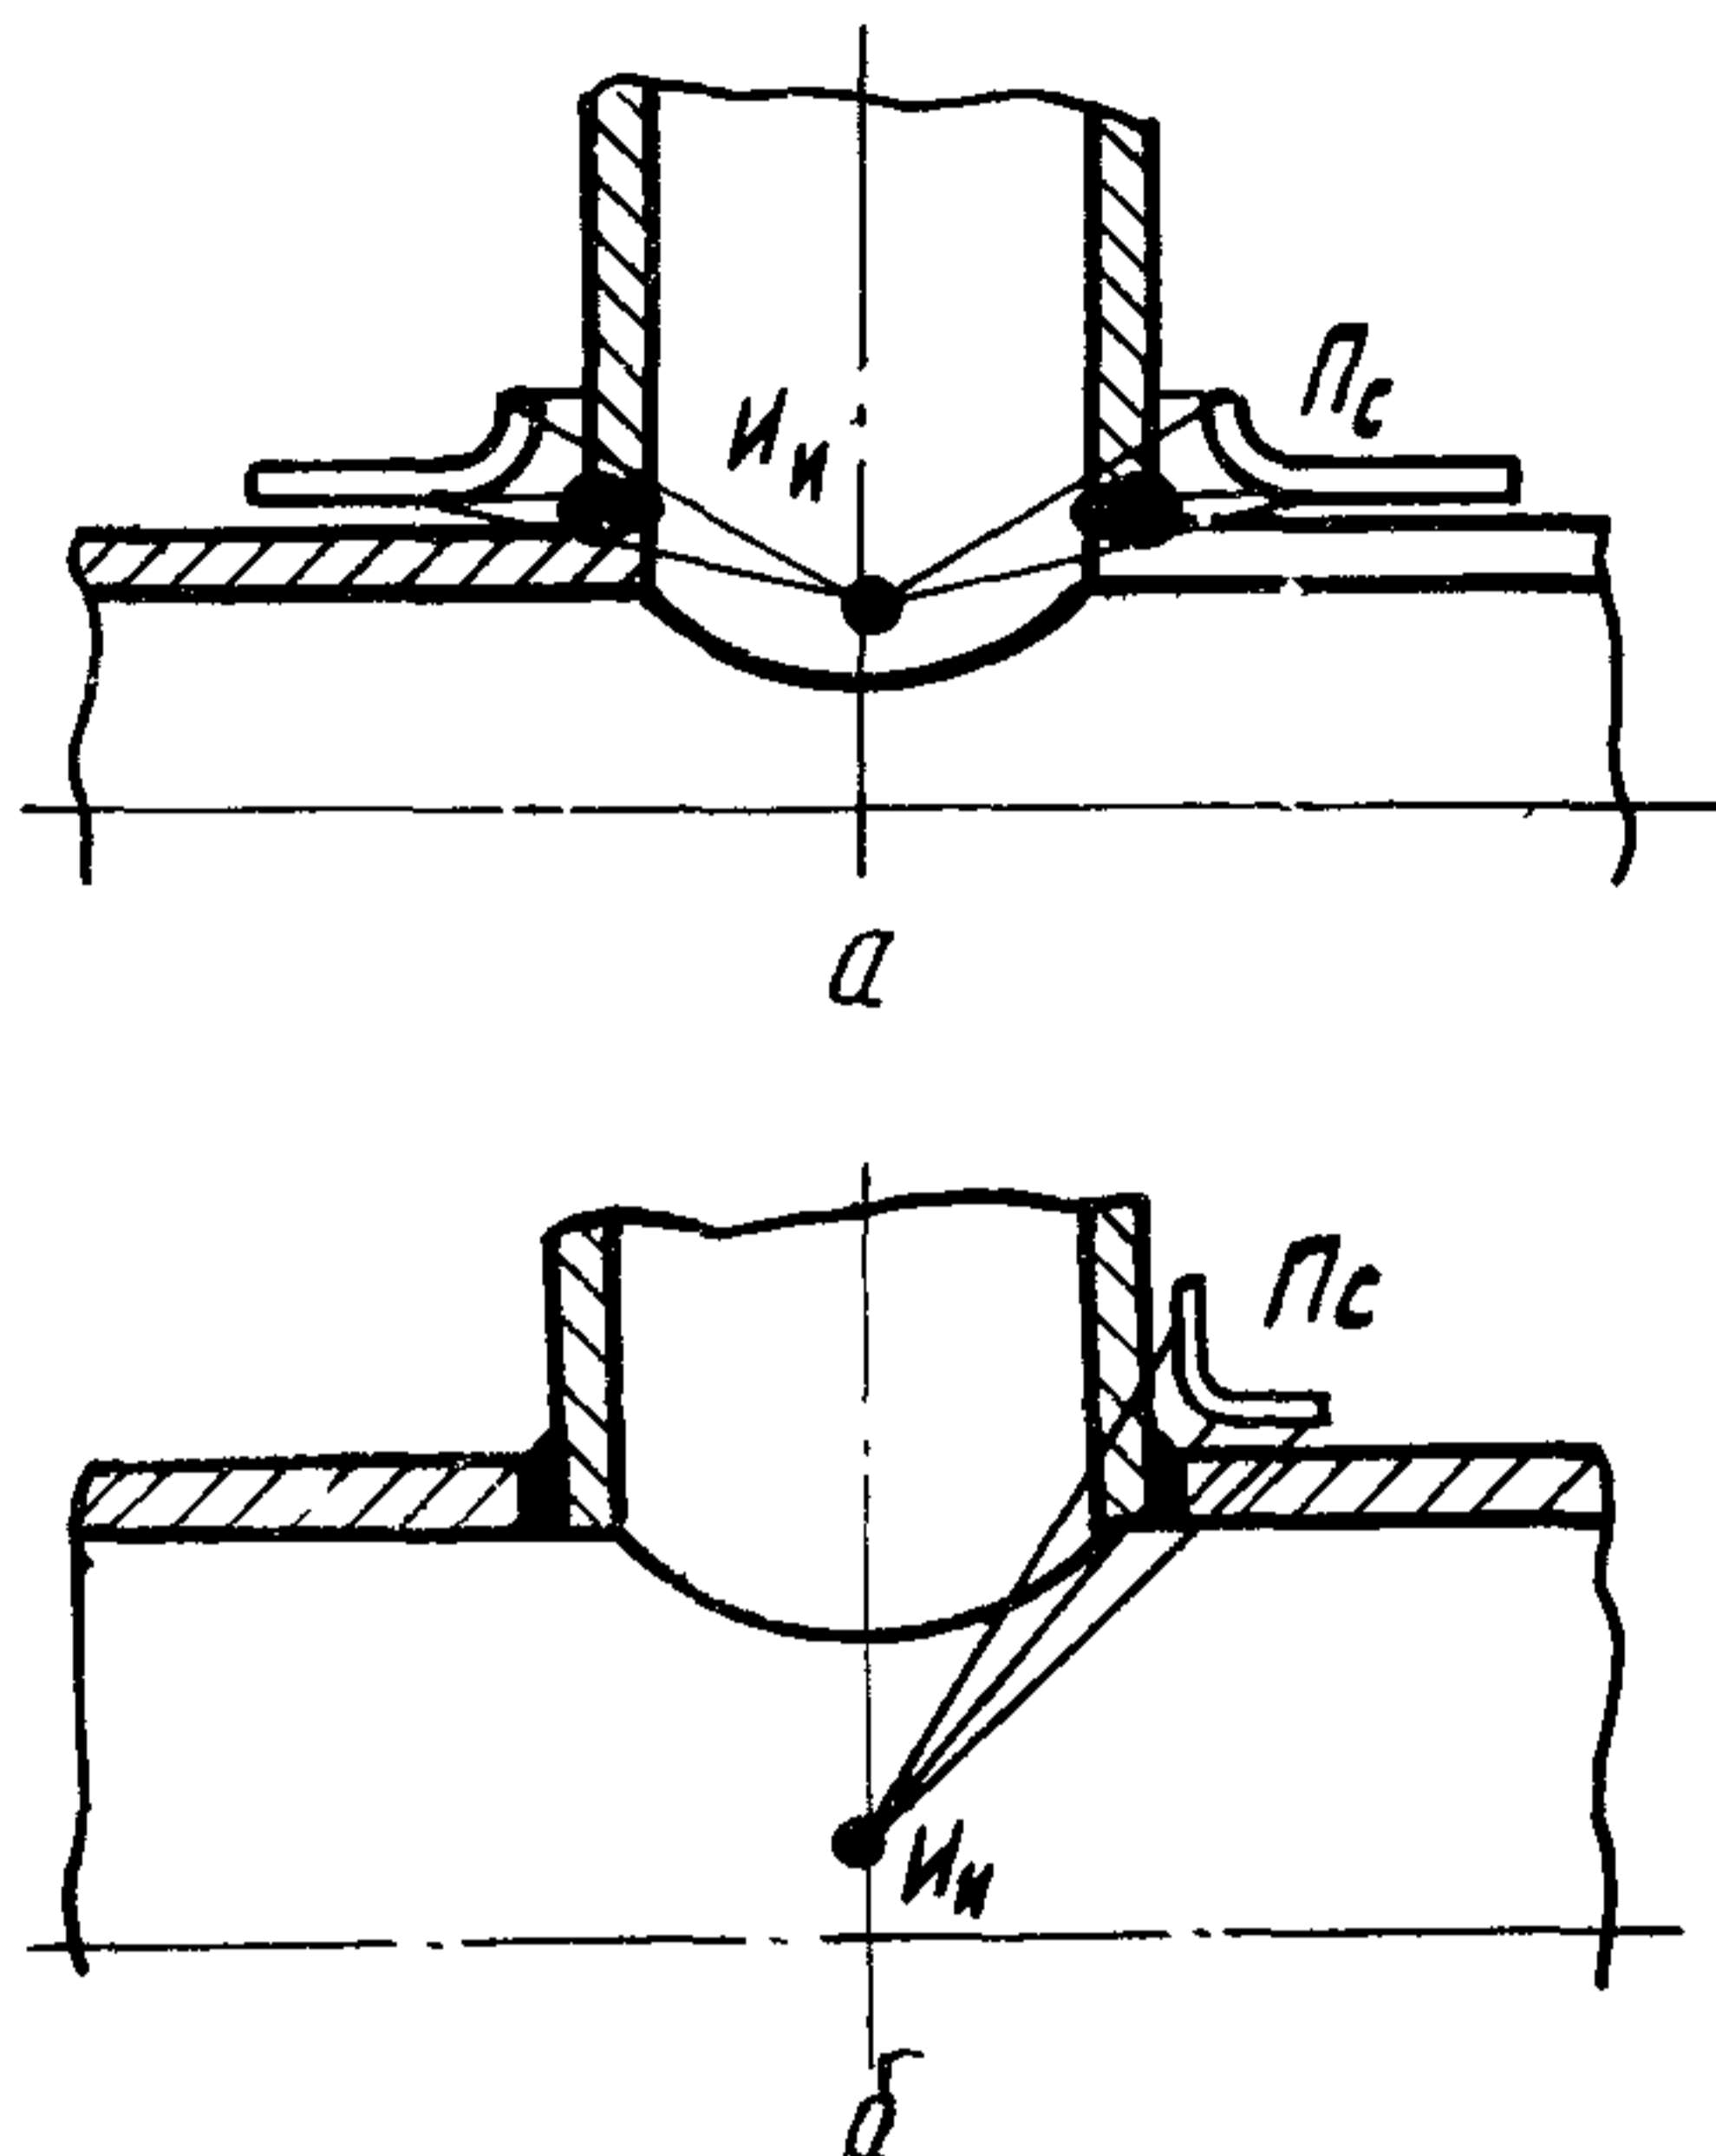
Схемы просвечивания криволинейного сварного шва изнутри:
